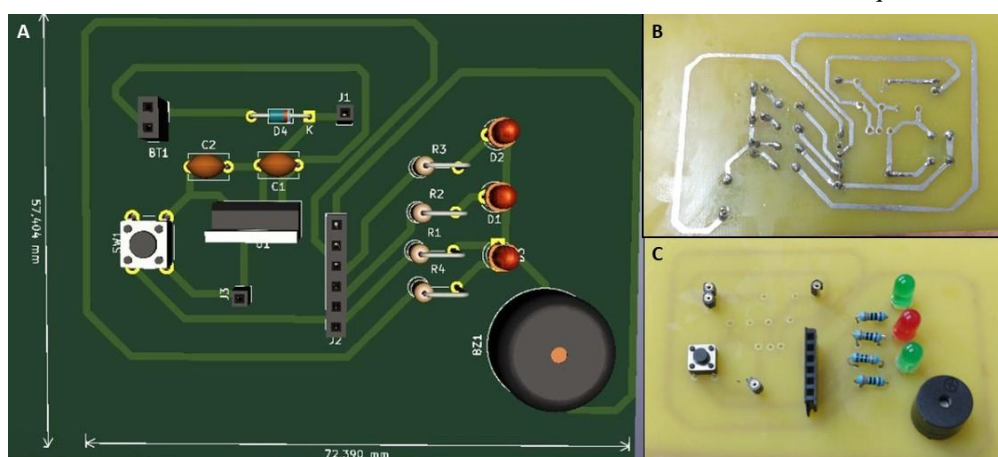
Ilustração do layout da PCB. Em (A) a simulação da placa em 3D gerada pelo software. Em (B) e (C) as partes inferiores e superiores da placa já confeccionada e soldada, respectivamente.
